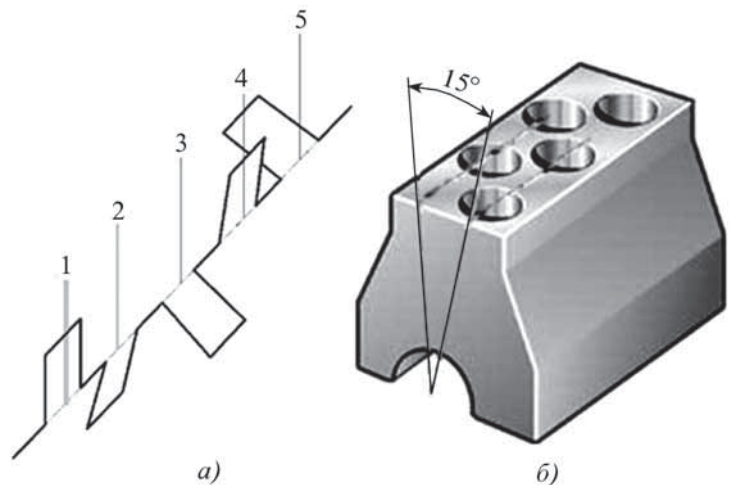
Схемы коленчатого вала (а) и блок-картера (б) двигателя типа VR5: 1–5 – оси цилиндров
